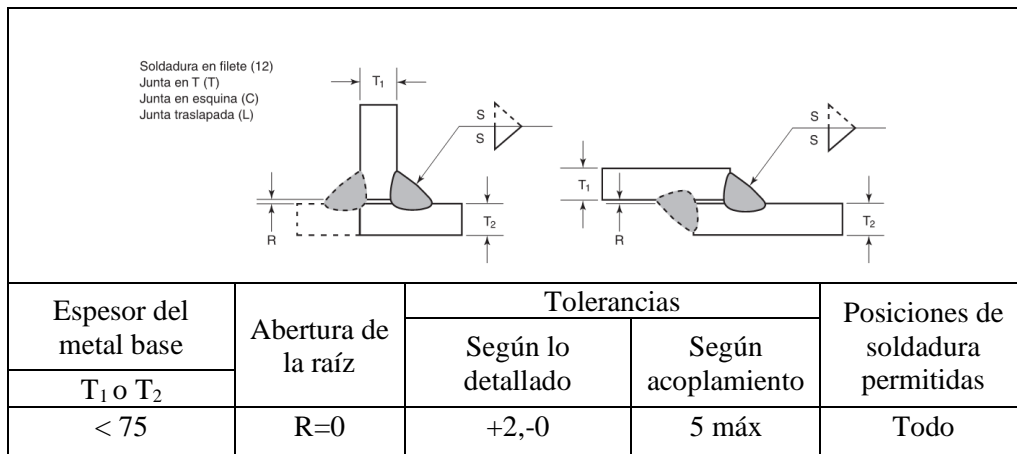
Detalles de la junta soldada en filete precalificada en milímetros
